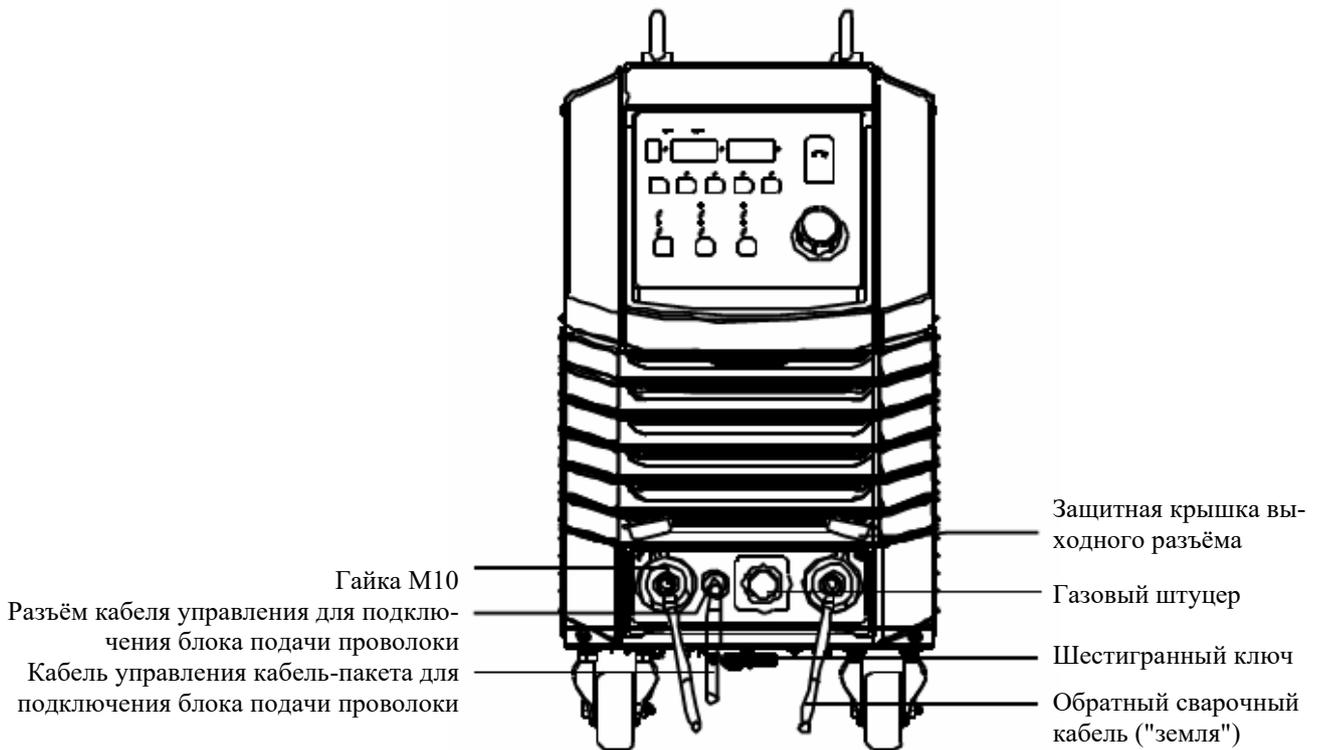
Принципиальная схема подключения выходных сварочных кабелей блока подачи проволоки и заготовки к положительному и отрицательному выходным разъёмам со сварочными силовыми кабелями
